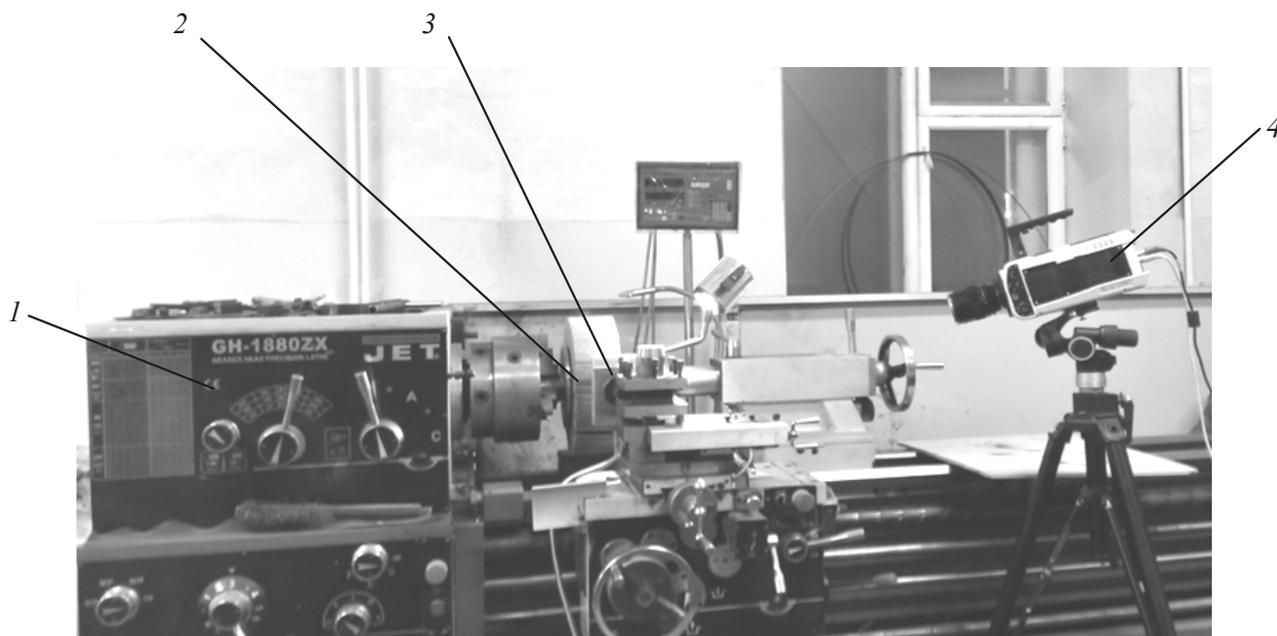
Комплекс для исследования характера контактных процессов лепесткового круга с поверхностью детали на токарном станке: 1 – токарный станок модели GH-1880ZXJET; 2 – лепестковый круг; 3 – резцедержатель с образцом; 4 – видеокамера модели Phantom v711
